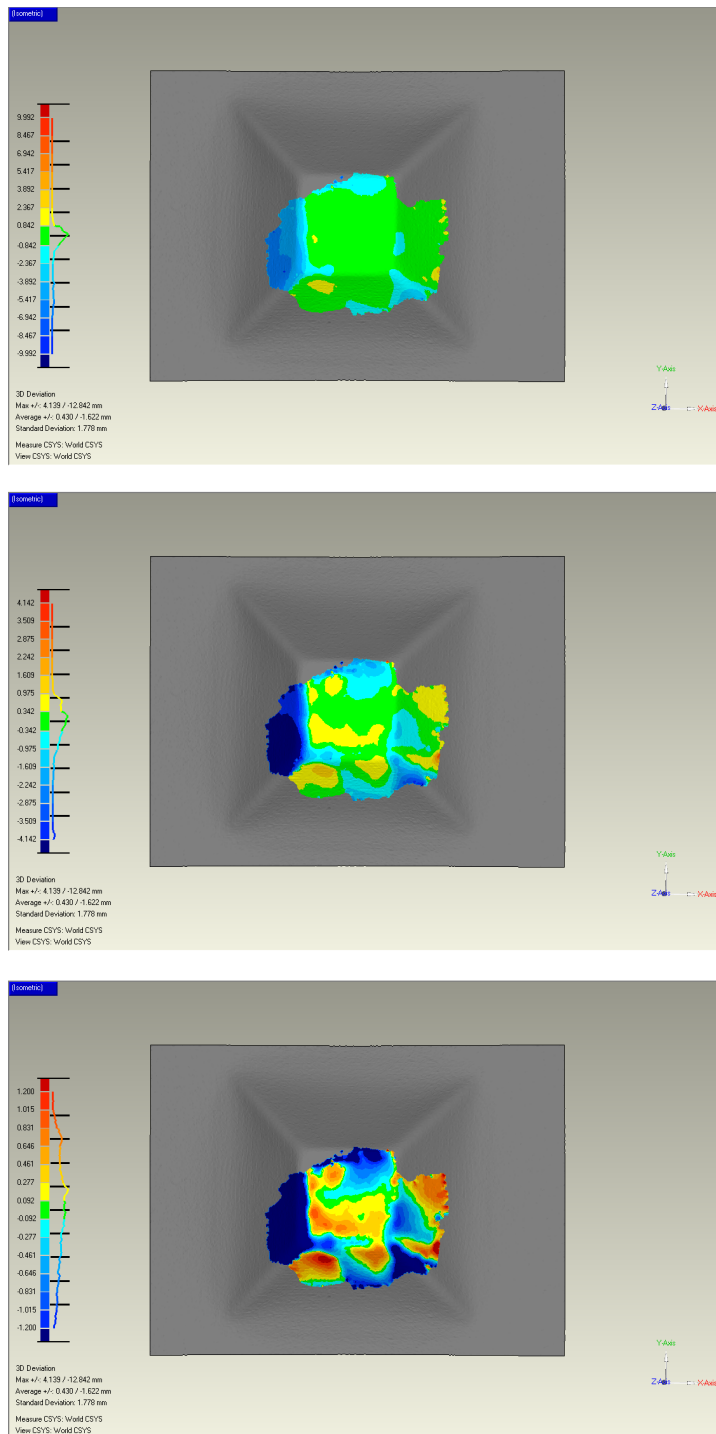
Erreur avec différentes échelles entre la reconstruction 3D avec des caméras infrarouges et la reconstruction de référence.
